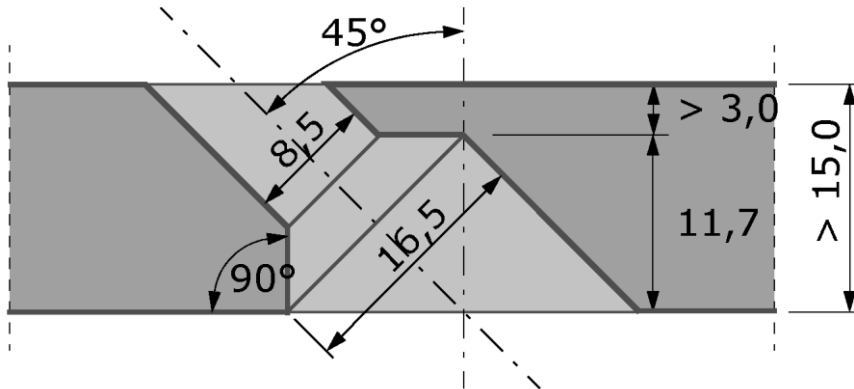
Bohrungsdetail mit Mindestabmessungen für Stahlbleche für eine Schraube mit dem Nenndurchmesser $d = 8 \text{ mm}$ und einem Winkel β von 45° (in mm)
